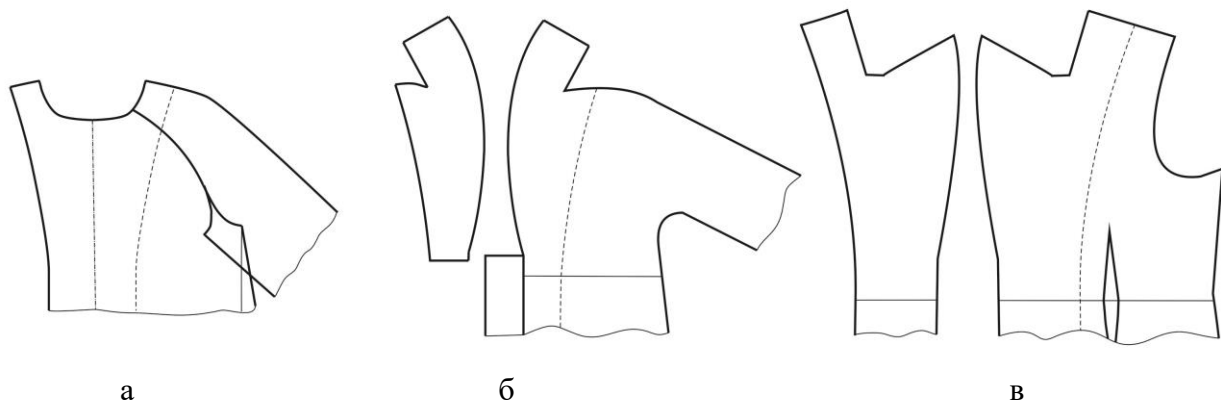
Виды конструкций подбортов в изделиях: а — цельнокроеный подборт; б — комбинированный подборт; в — отрезной подборт.
